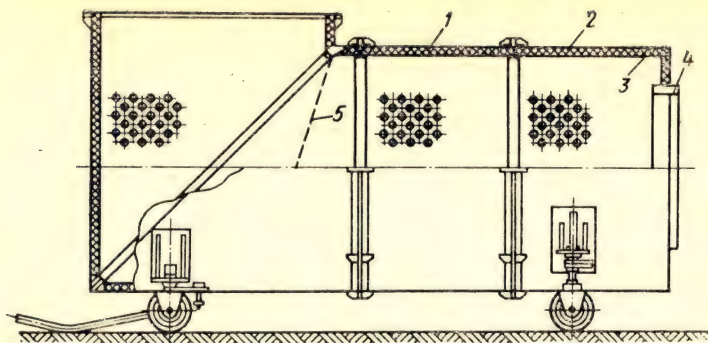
Схема устройства передвижного глушителя со стороны всасывания:
